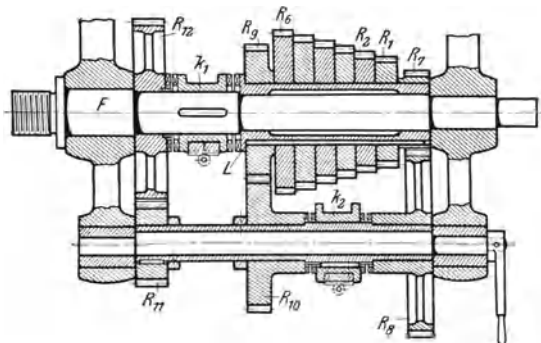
Stufenräderantrieb der Fräsmaschine.
